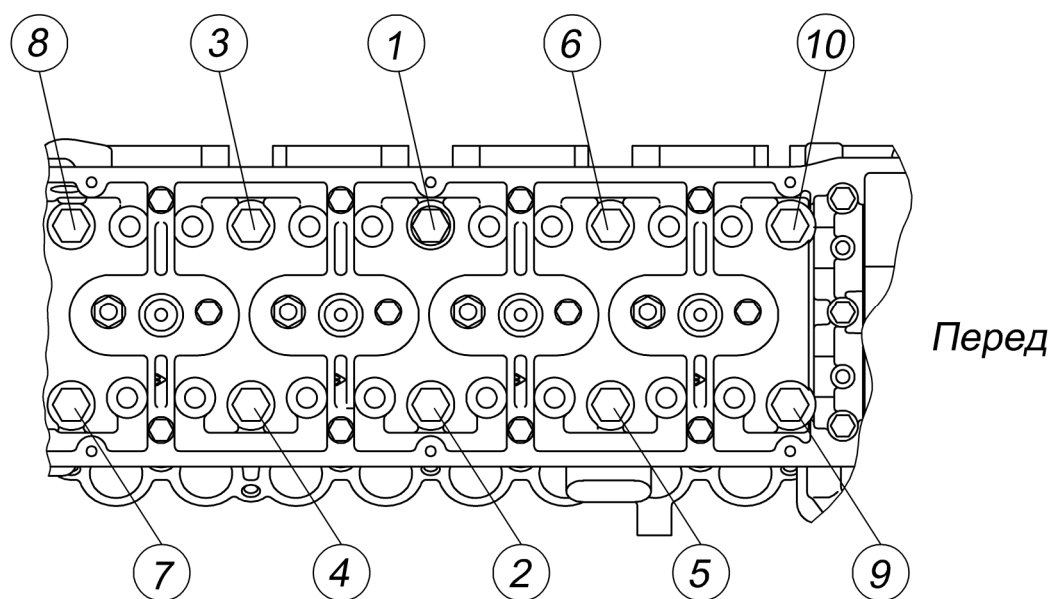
Последовательность затяжки болтов крепления головки цилиндров
